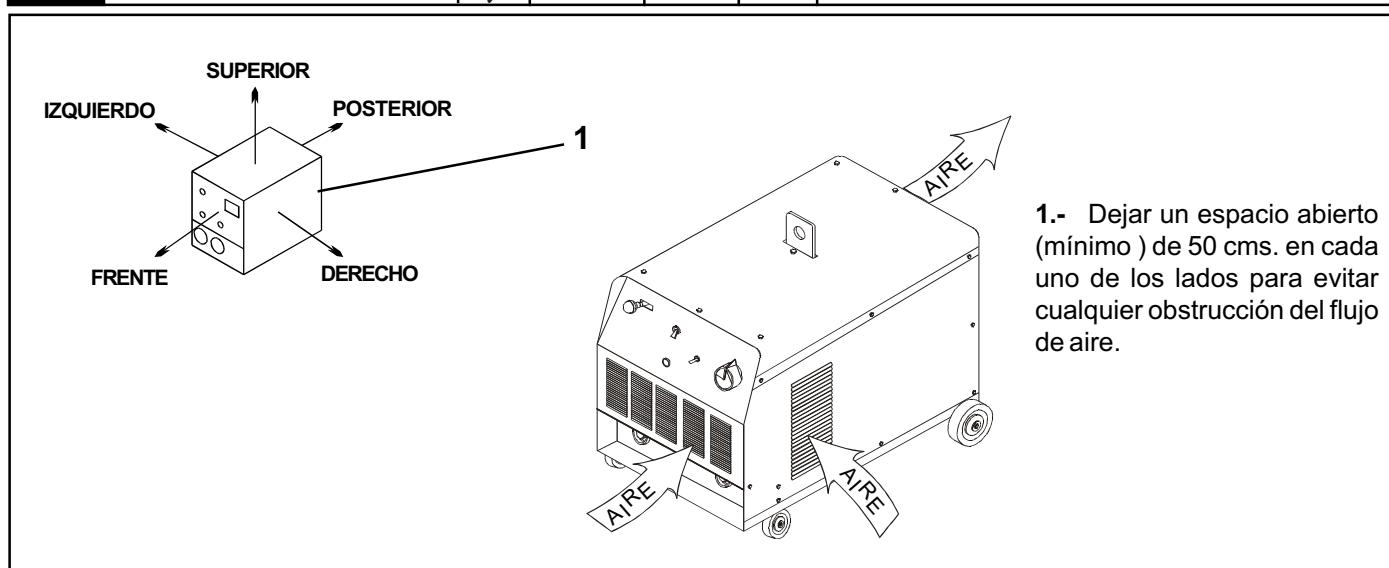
LOCALIZACION Y MOVIMIENTO DE LA MAQUINA SOLDADORA
